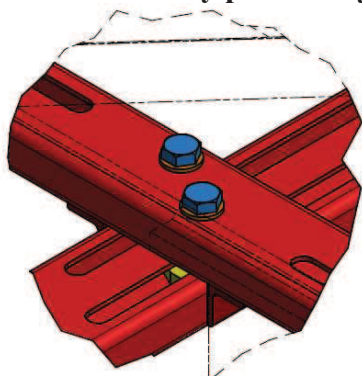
Izometrický pohled na přípravek s vloženým stožárovým dílem.
